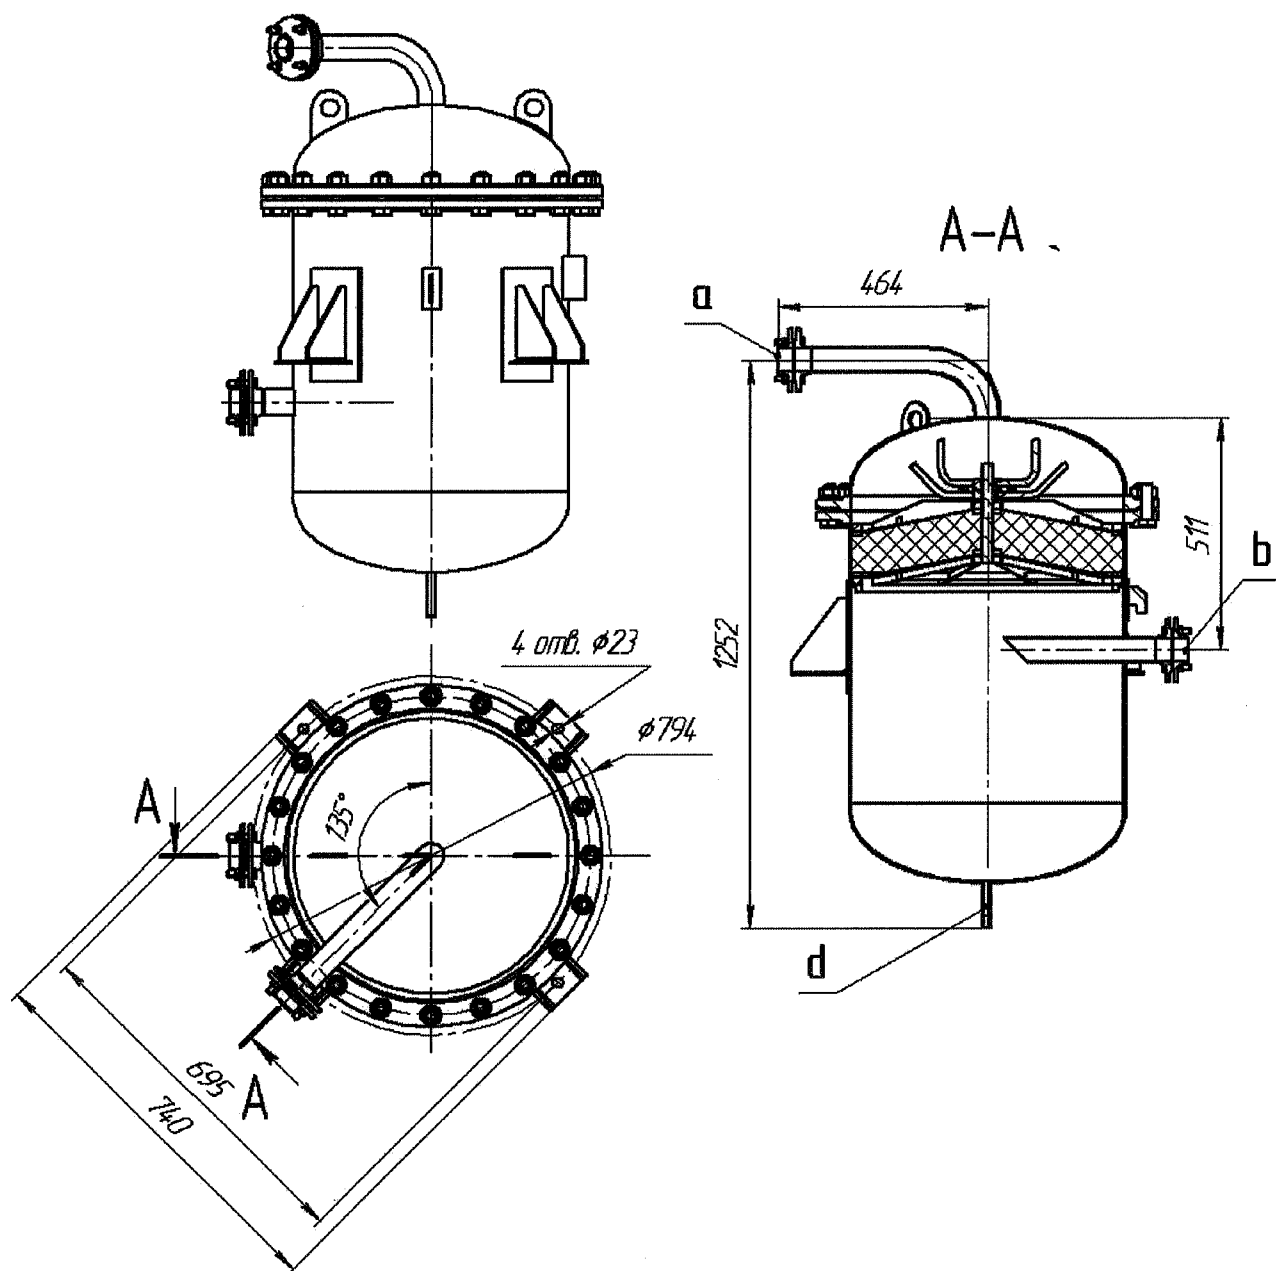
Габаритный чертеж фильтра аэрозольного KPL70AT001, KPL70AT003
